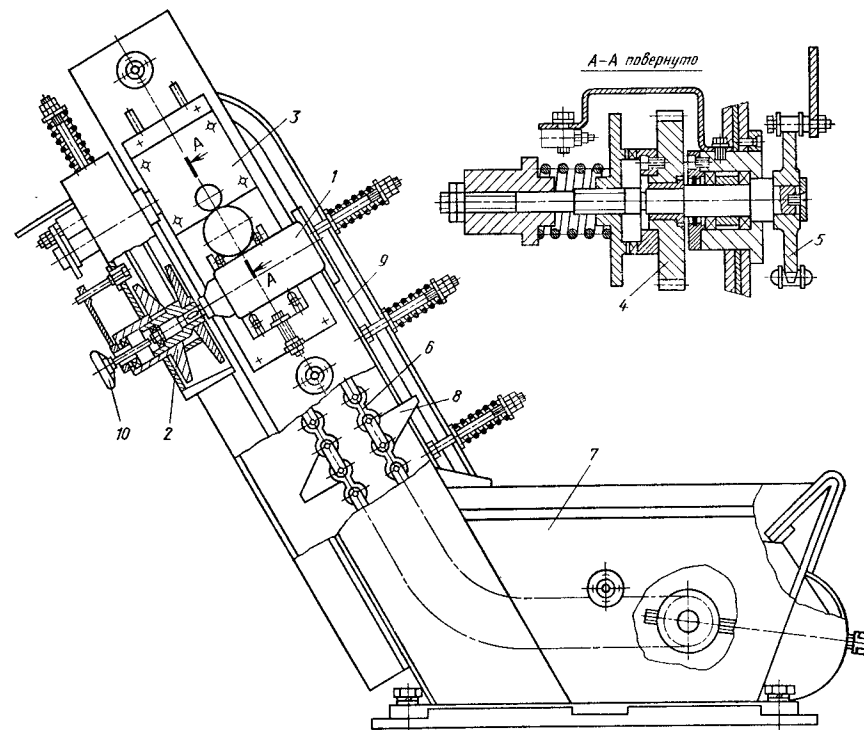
Бункерно-загрузочное устройство резьбонакатного автомата с плоскими плашками
